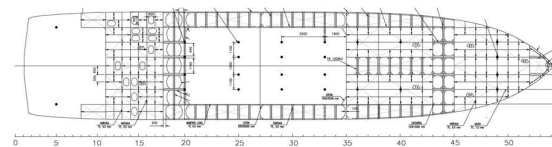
Cubierta de doblefondo. Fuente: elaboración propia
